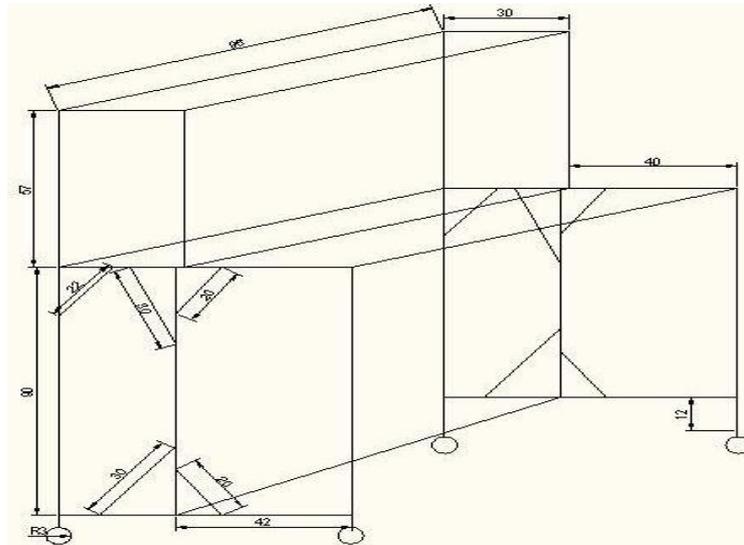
ELABORACIÓN DEL PLANO DEL BANCO
